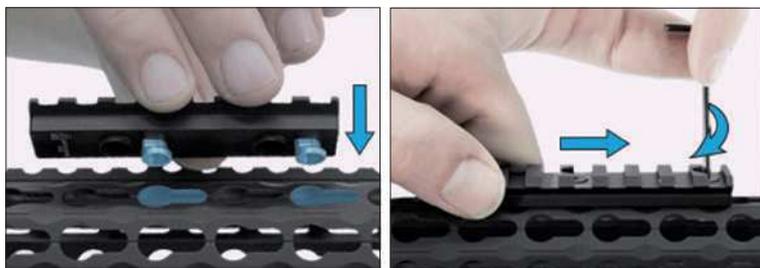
Планка KeyMod, для кріплення додаткового обладнання
